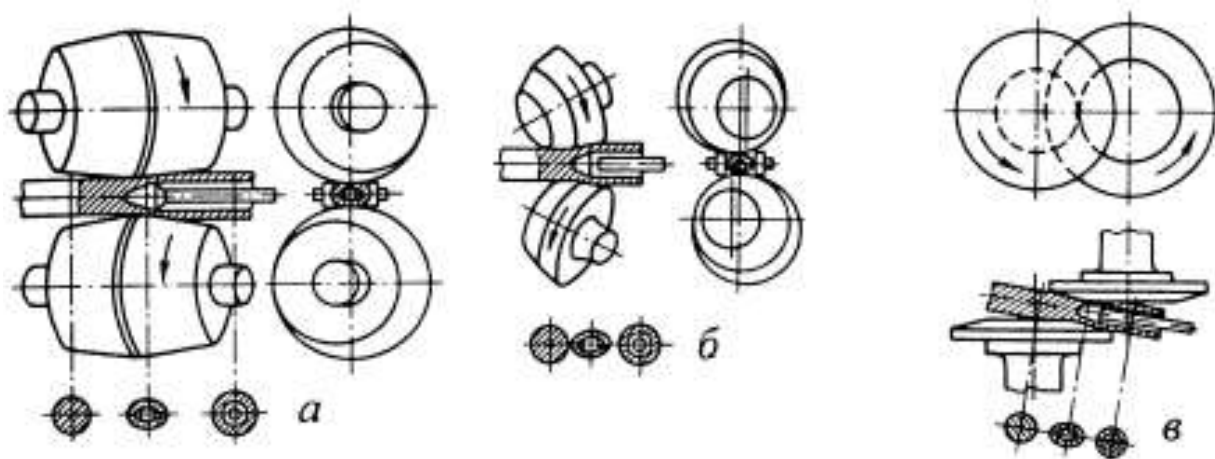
Схемы прошивки заготовок в двухвалковых станах винтовой прокатки [12]:
